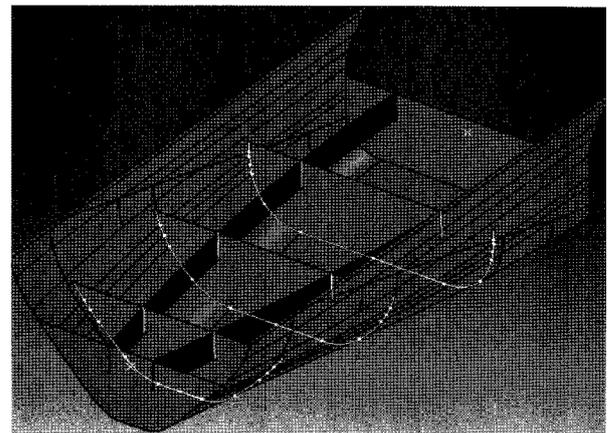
선체 블록의 3D CAD 형상 모델 (Beam과 Plate의 복합 모델)
